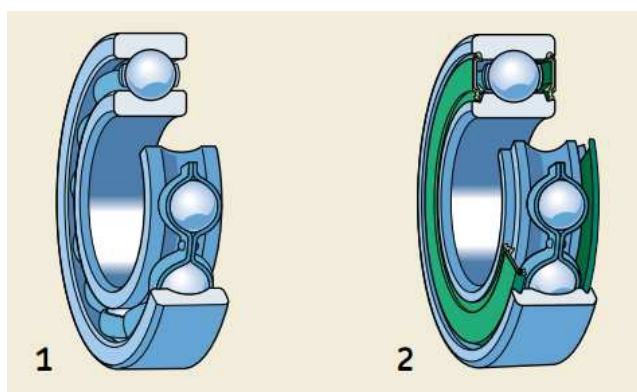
Rodamiento de bolas de una hilera sin obturador (izq.) y con obturador (dcha.).
